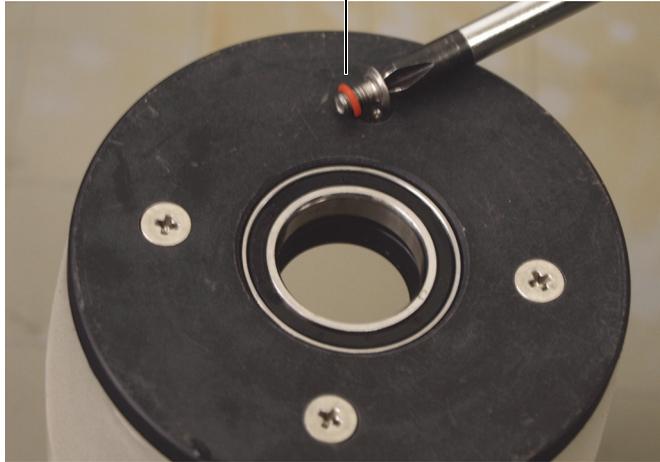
Entfernen der äußeren Halteschrauben vom Flachflansch
